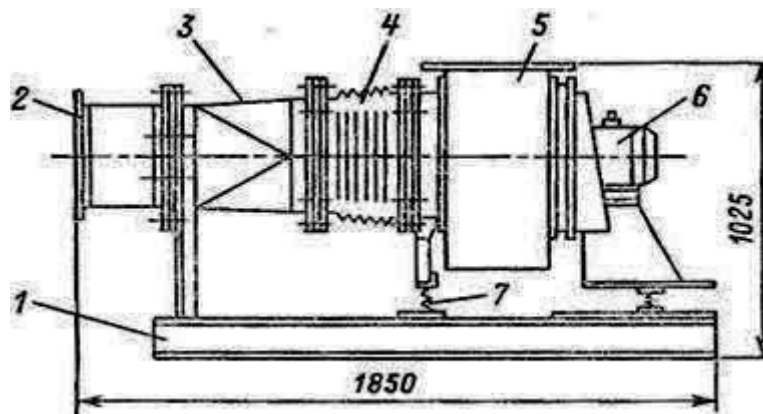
Общий вид электрокалориферной установки типа СФОА:
